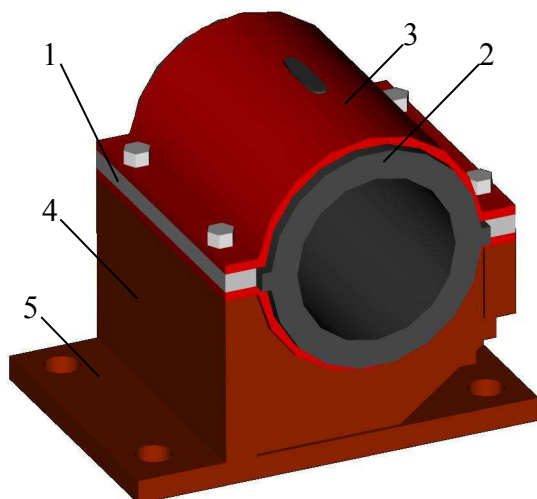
Експериментальний підшипник вала соломотряса: 1 – прокладка; 2 – напівпідшипники; 3 – каркас; 4 – корпус; 5 – основа
